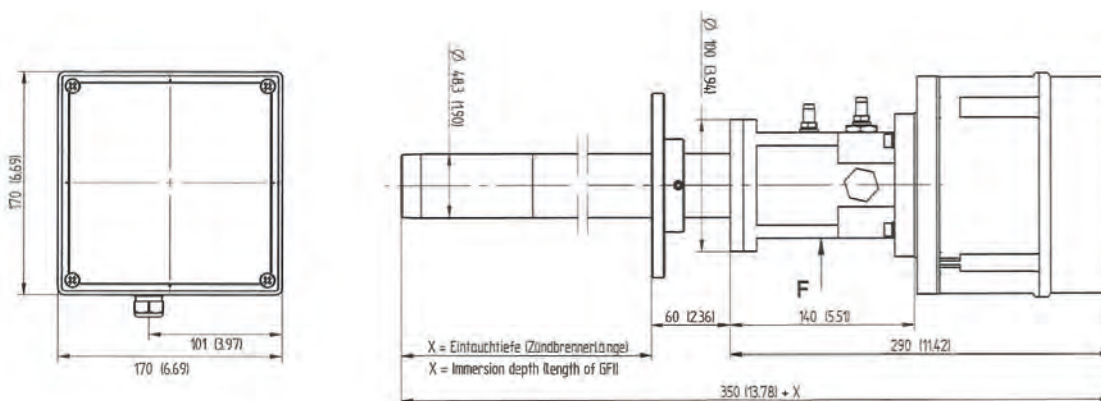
Dimensões do queimador de ignição GFI48 para zona Ex 2
